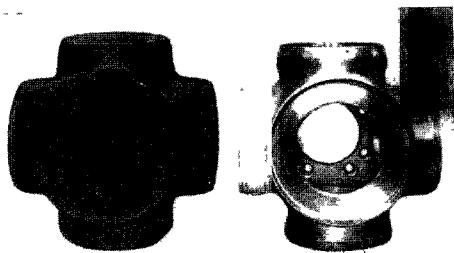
Обработка корпуса втулки в специальном приспособлении.
